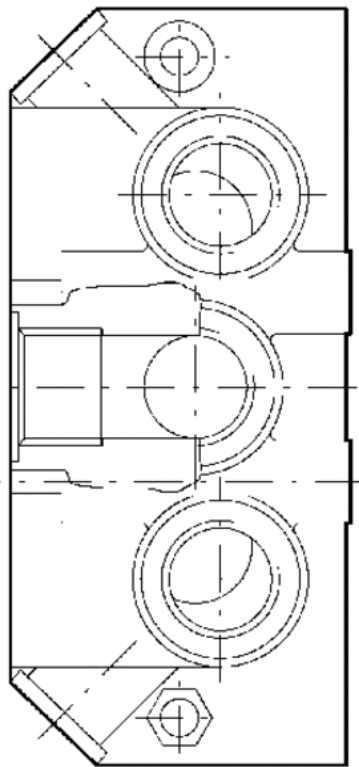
, Gewindeanschlüsse 1, 3 und 5 axial
